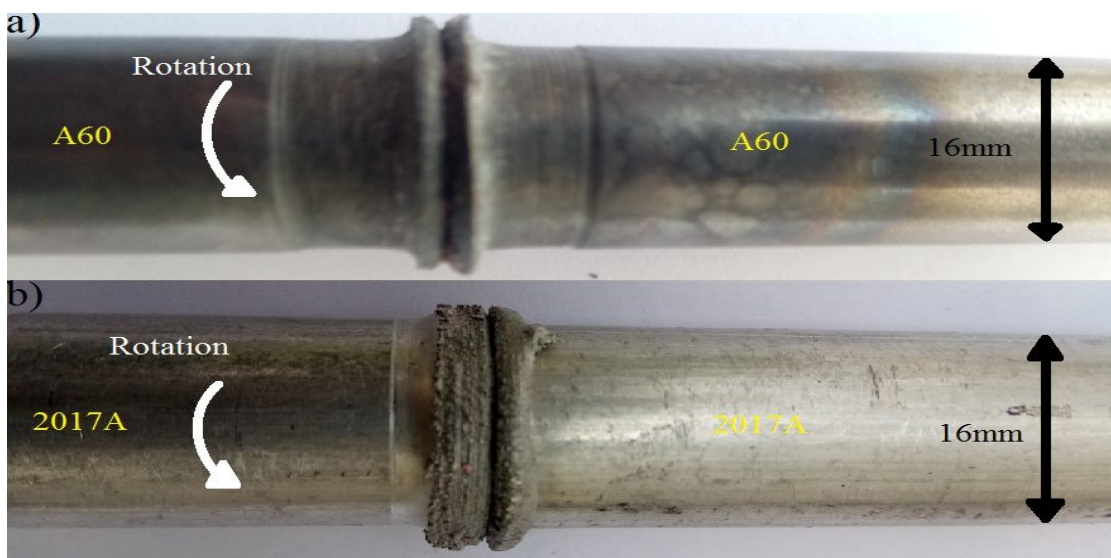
Macrographie de deux éprouvettes soudées par friction. (a) Acier A60/Acier A60 (N=1400tr/min, t=30s). (b) Al 2017A/Al 2017 (N=1400 tr/min, t=30s).
